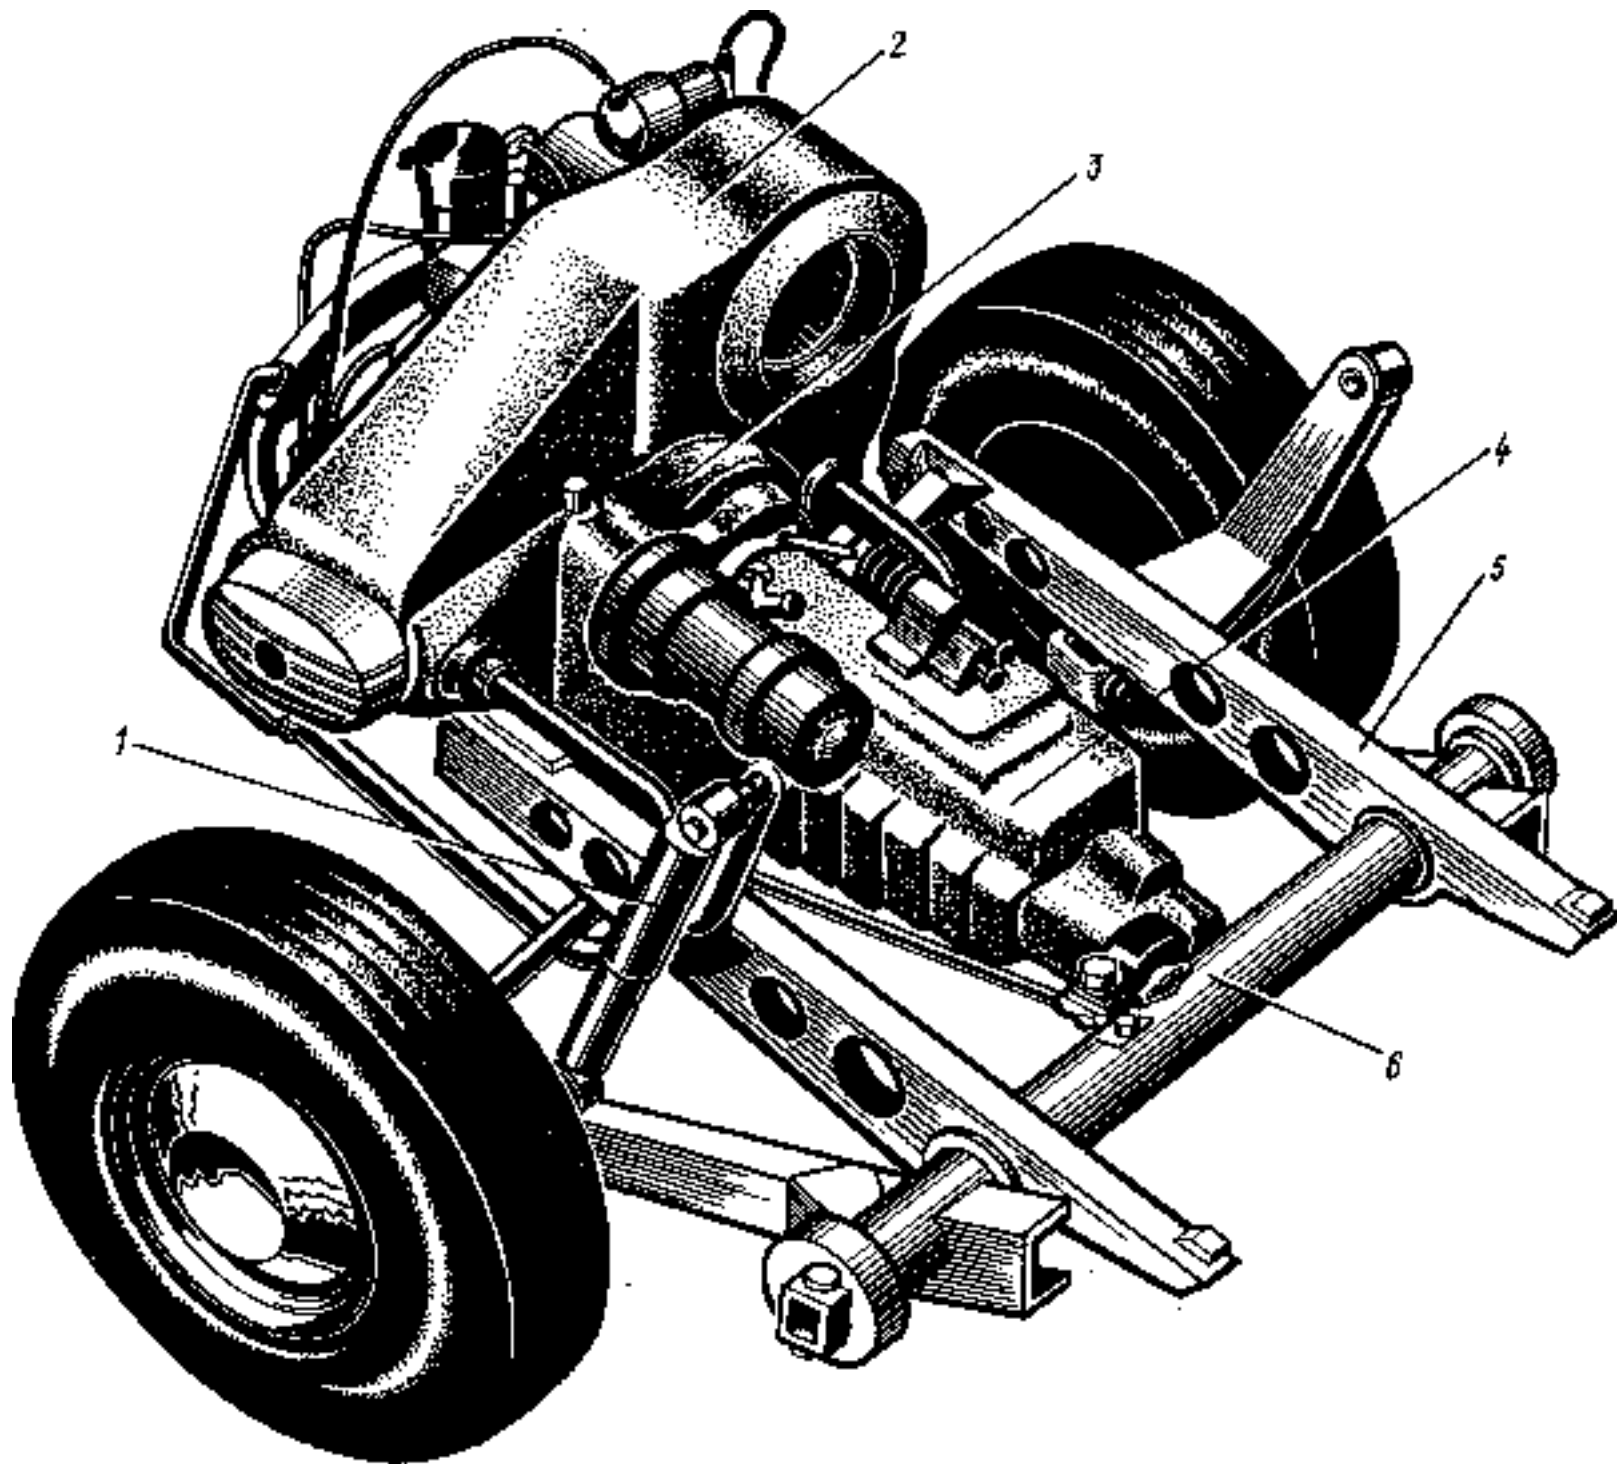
Универсальный силовой агрегат для микроавтомобиля:
